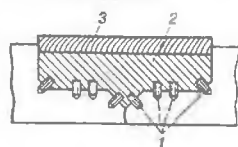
Підготовка чавунного виробу до холодного зварювання з сталевими шпильками:
